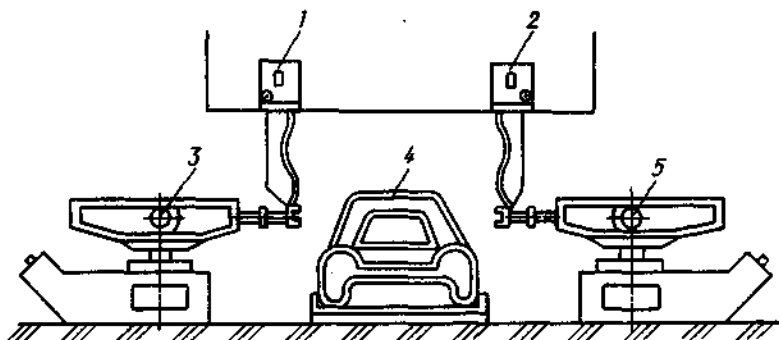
Схема сварочного участка на автоматической линии сборки кузовов автомобилей:
